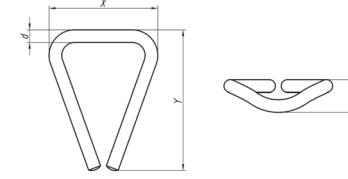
Габаритные размеры фиксатора волнообразного L2.1П.
